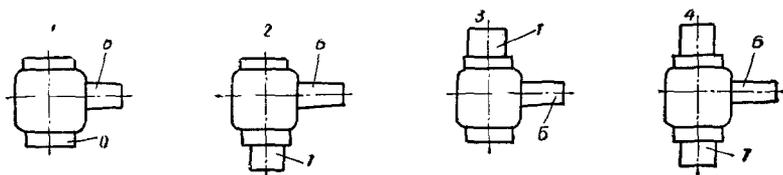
Схемы сборки (1—4) редукторов РЧУ:
